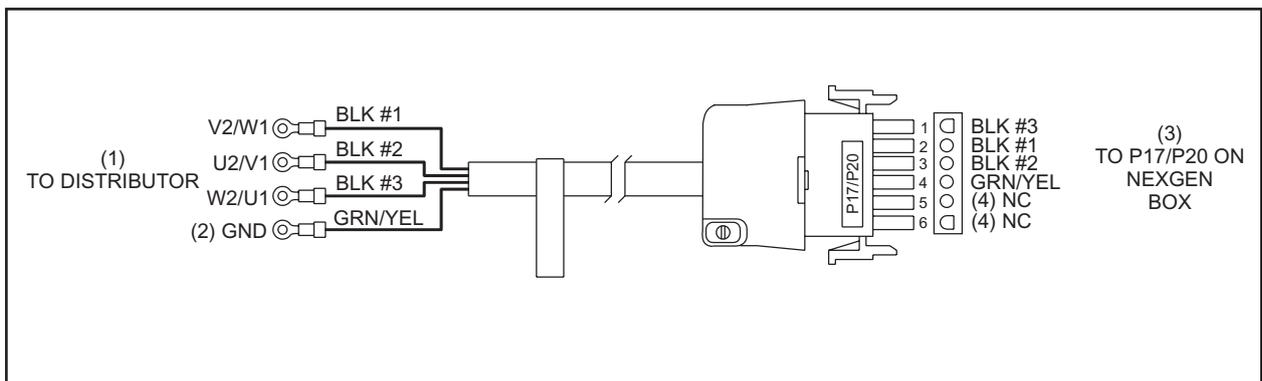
Ensemble câble moteur de distributeur externe (Pièce N° 47-142616-000)
